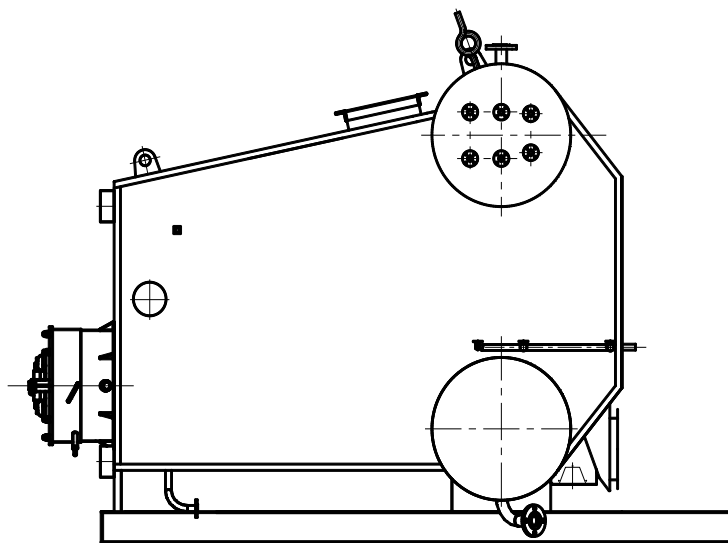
Общий вид котла E-1,0-0,9 работающего на твердом топливе
